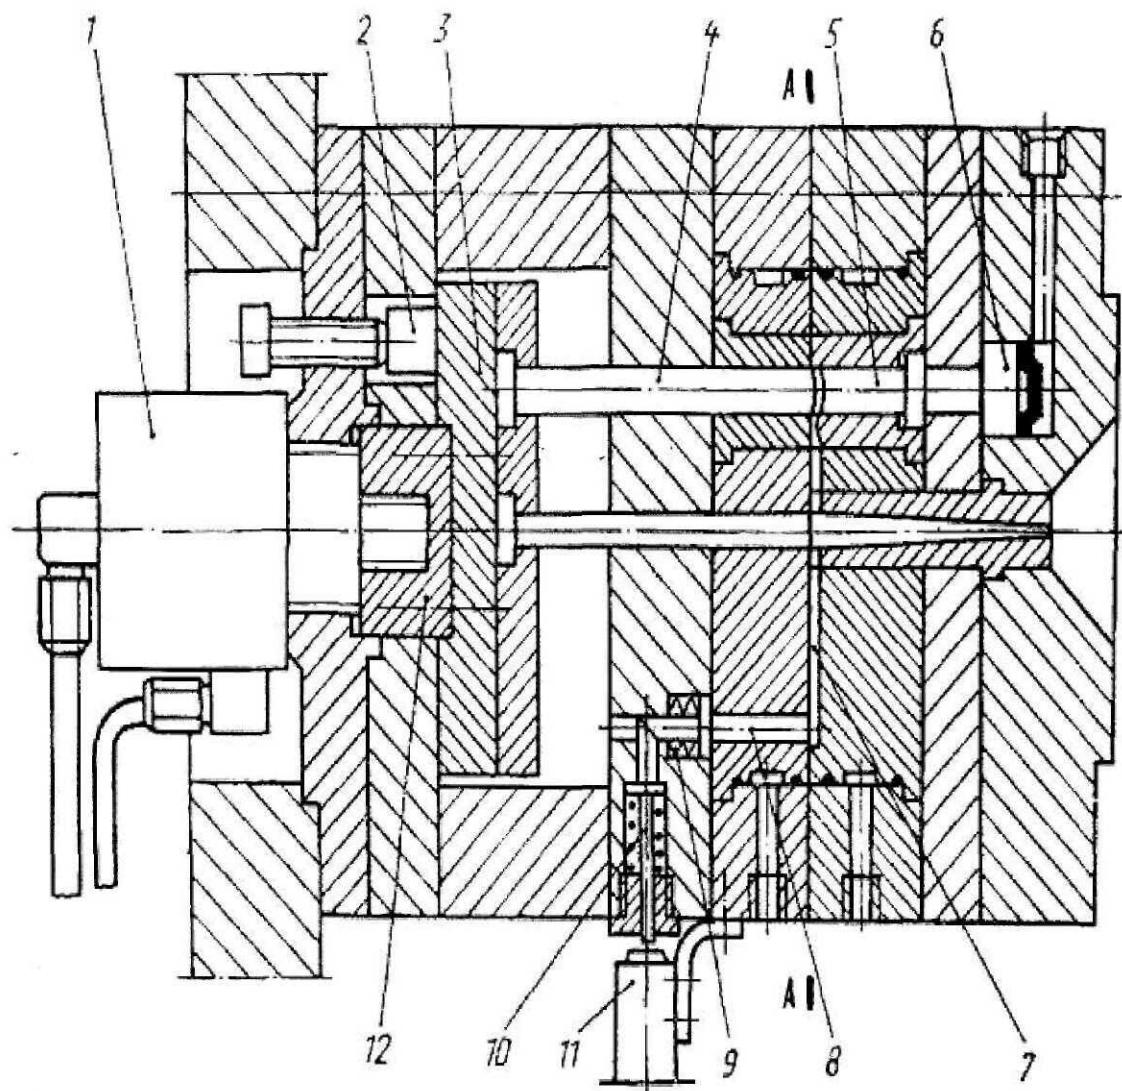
Пресс-форма литьевая с двухсторонней гидравлической подпрессовкой:
